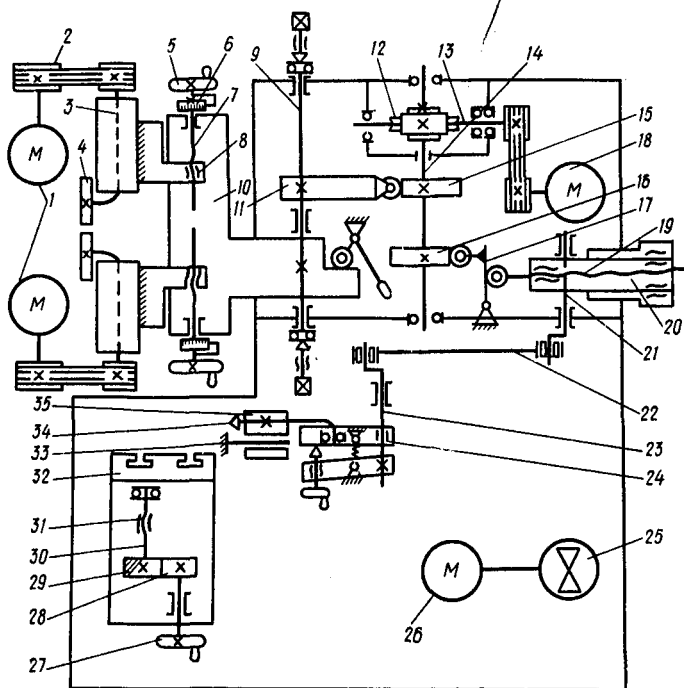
Кинематическая схема станка ТчПБ для боковой заточки зубьев пил:
